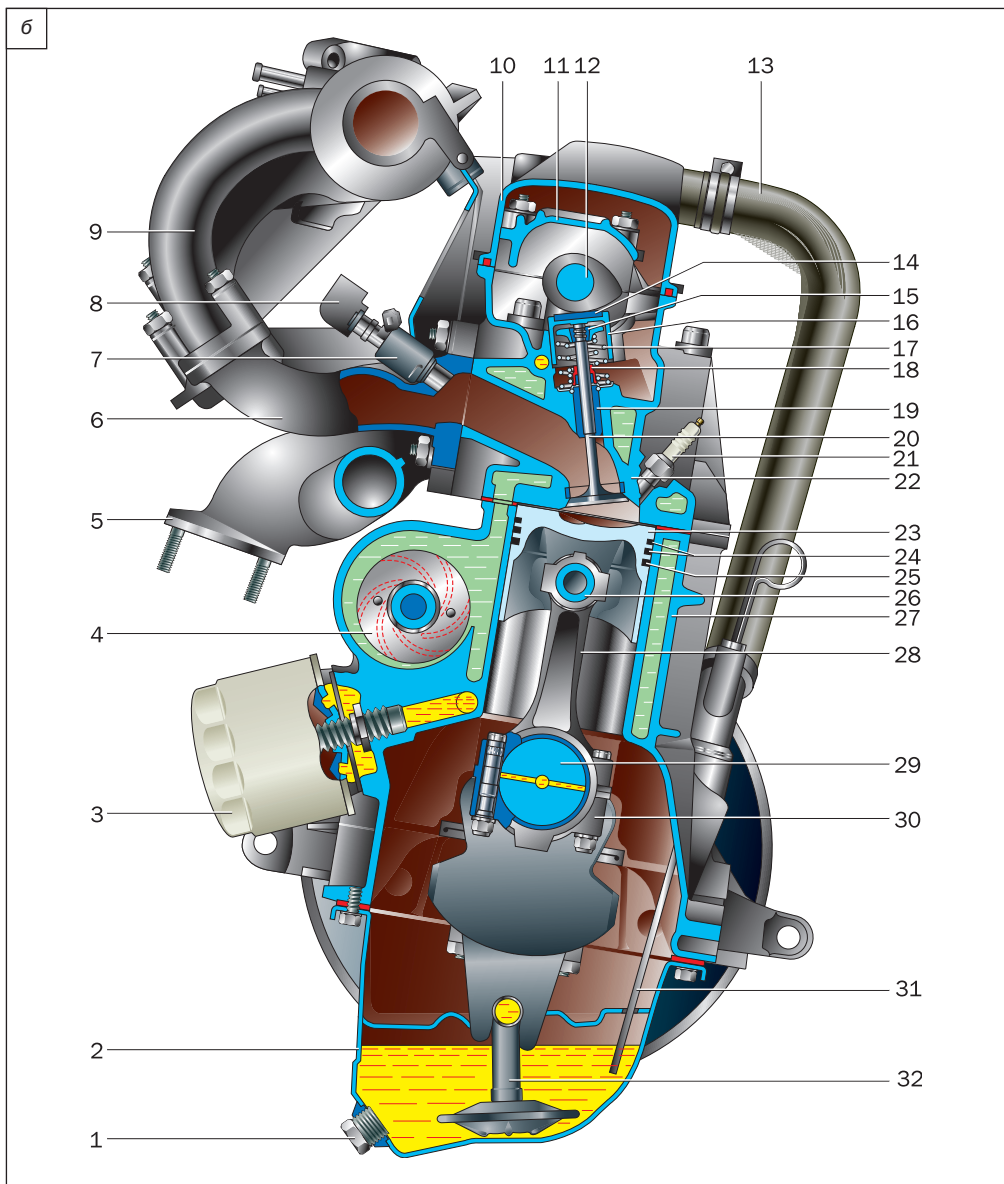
б. Поперечный разрез двигателя ВА3-2111: 1 — пробка сливного отверстия поддона картера; 2 — поддон картера; 3 — масляный фильтр; 4 — насос охлаждающей жидкости; 5 — выпускной коллектор; 6 — впускной коллектор; 7 — форсунка; 8 — топливная рампа; 9 — ресивер; 10 — крышка головки блока цилиндров; 11 — крышка подшипников распределительного вала; 12 — распределительный вал; 13 — шланг вентиляции картера; 14 — регулировочная шайба клапана; 15 — сухари клапана; 16 — толкатель; 17 — пружины клапана; 18 — маслосъемный колпачок; 19 — направляющая втулка клапана; 20 — клапан; 21 — свеча зажигания; 22 — головка блока цилиндров; 23 — поршень; 24 — компрессионные кольца; 25 — маслосъемное кольцо; 26 — поршневой палец; 27 — блок цилиндров; 28 — шатун; 29 — коленчатый вал; 30 — крышка шатуна; 31 — указатель уровня масла; 32 — приемник масляного насоса
